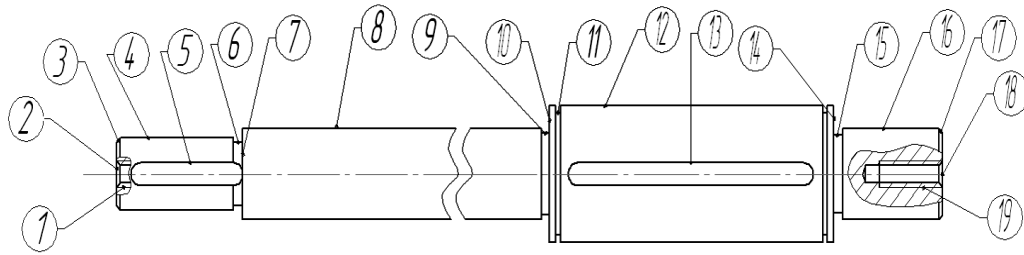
Технологічна розмітка поверхонь деталі
